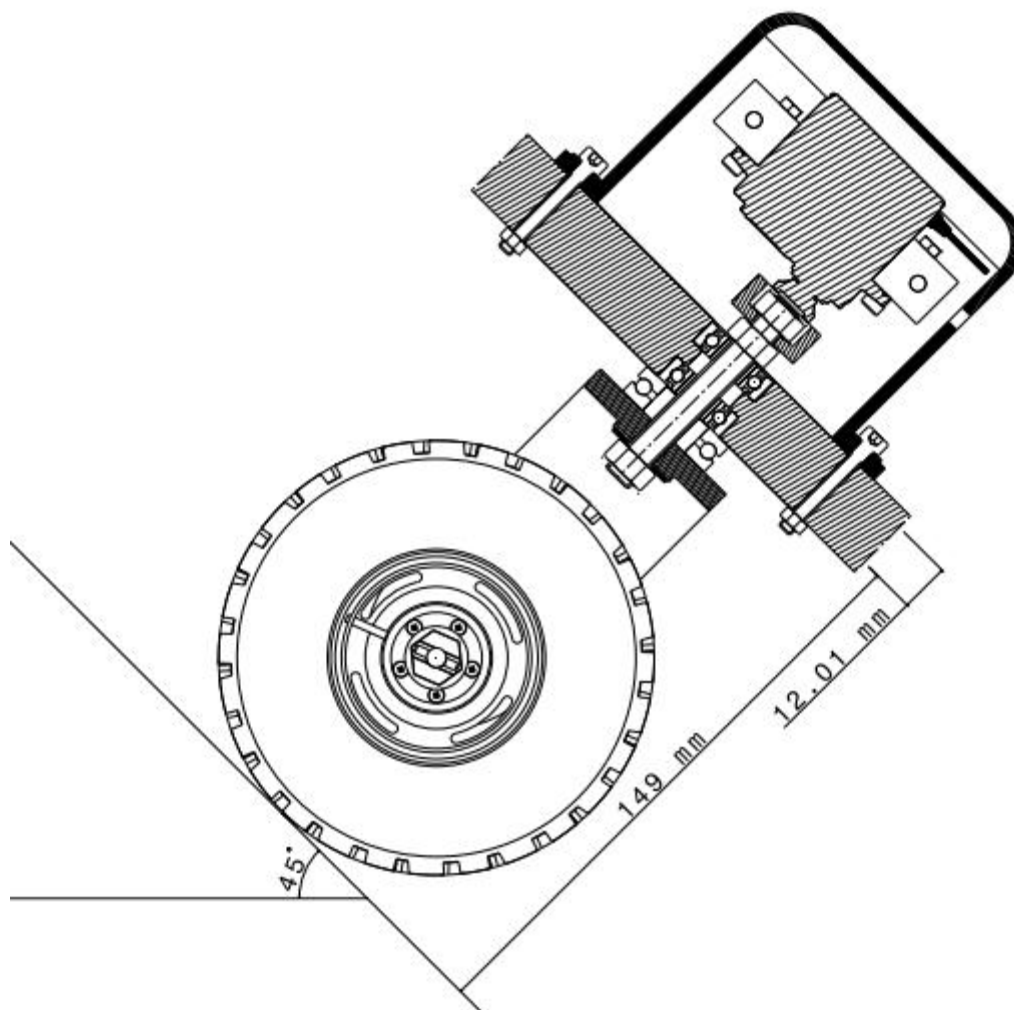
Vista en sección del conjunto, cuando este se sitúa trabajando en una pendiente.
